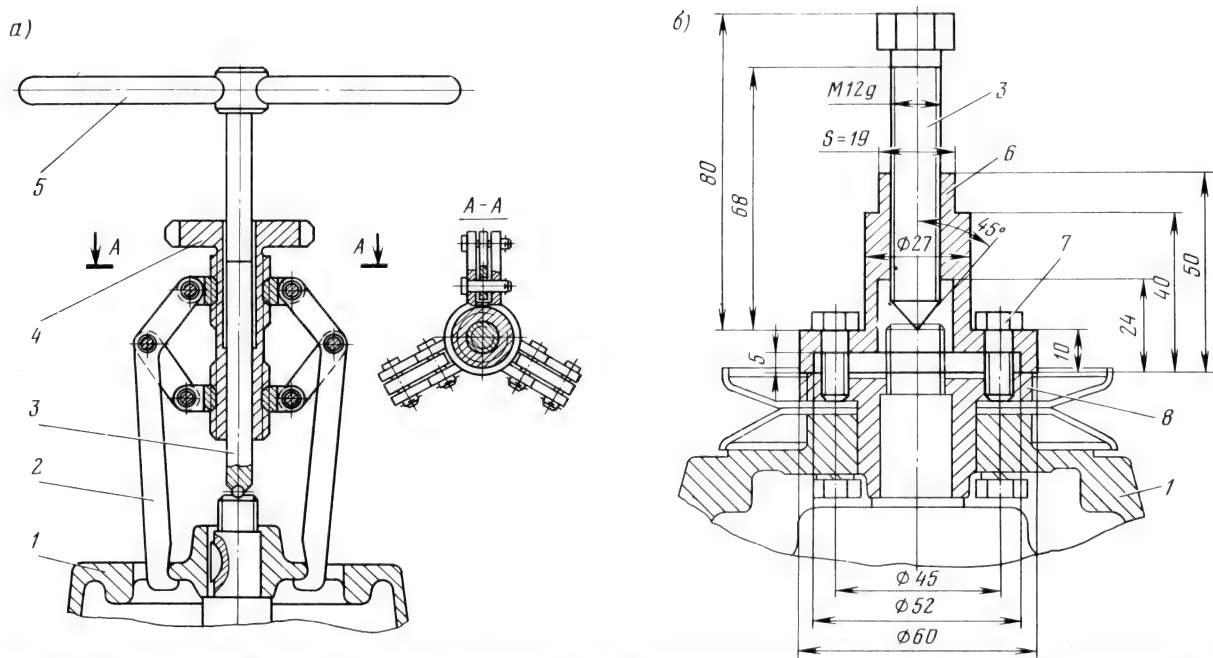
Съёмники рабочего колеса вентилятора с вала генератора двигателя МеМЗ-966Г, работающего на нагнетание (а) и МеМЗ-966В, работающего на отсос (б);
